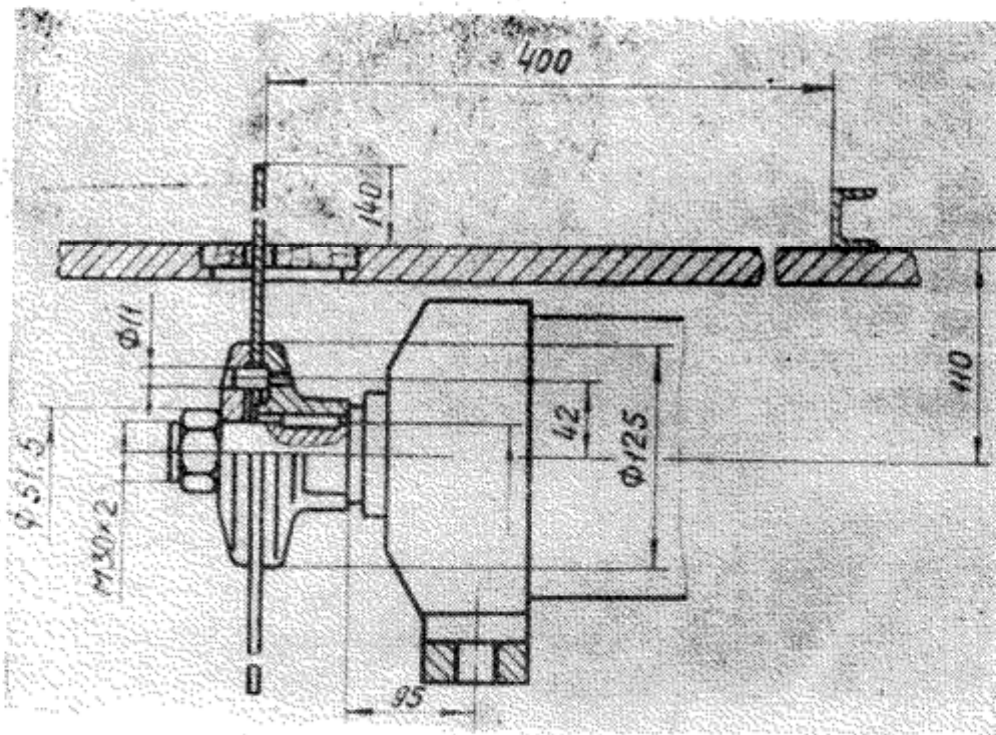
Габаритные размеры рабочего пространства и посадочные базы станка
